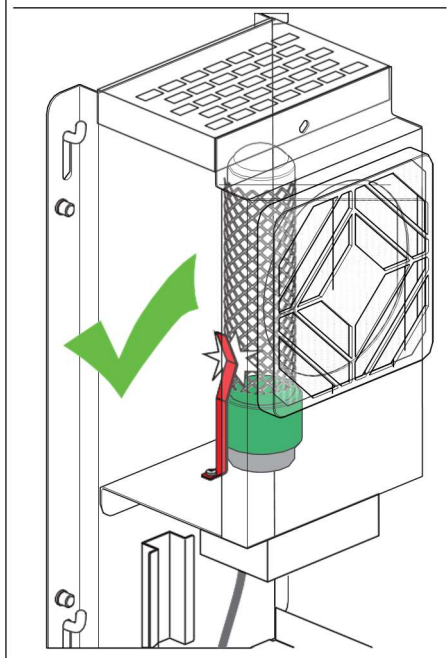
Réassembler le couvercle et le fixer avec ses vis.
